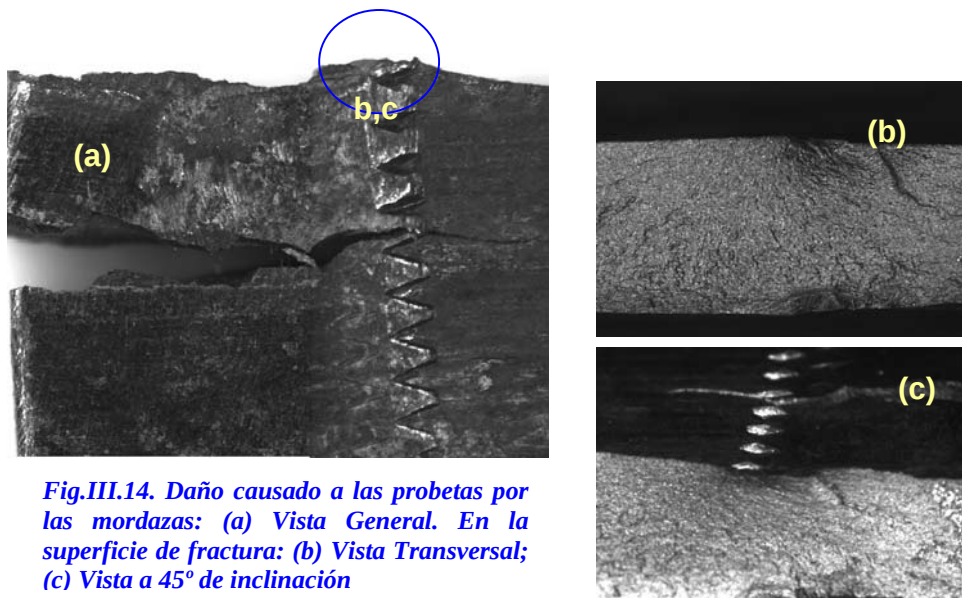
Daño causado a las probetas por las mordazas: (a) Vista General. En la superficie de fractura: (b) Vista Transversal; (c) Vista a 45° de inclinación
